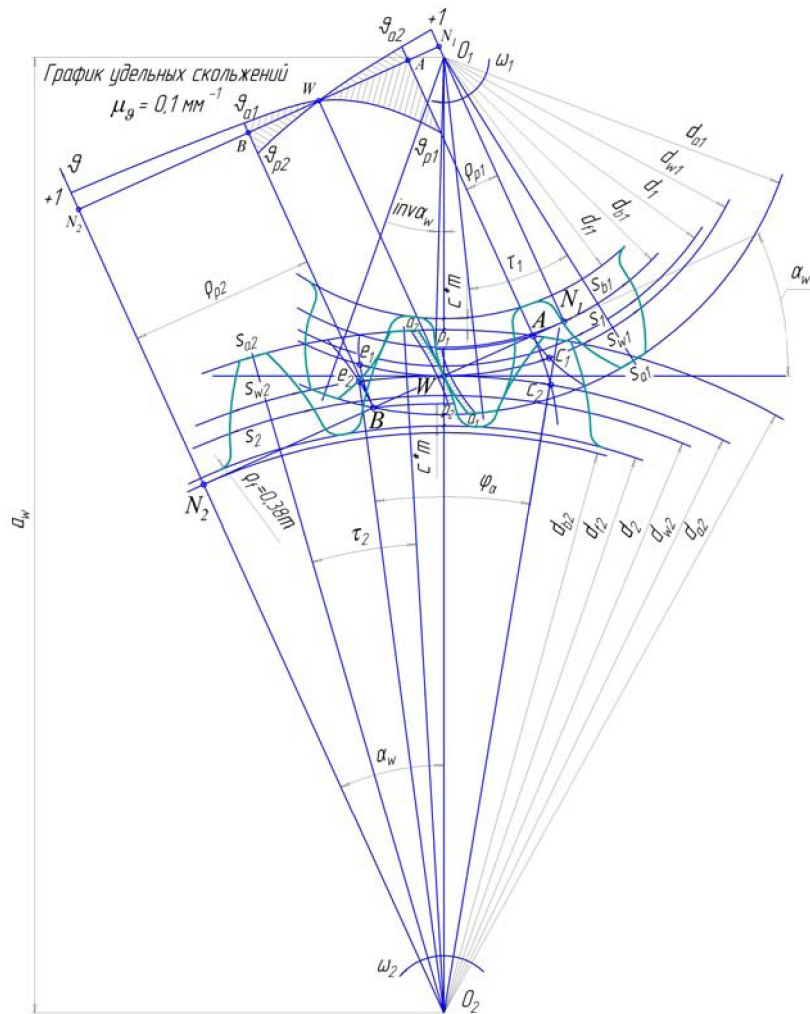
Схема зацепления цилиндрической пары колес с эвольвентными зубьями
